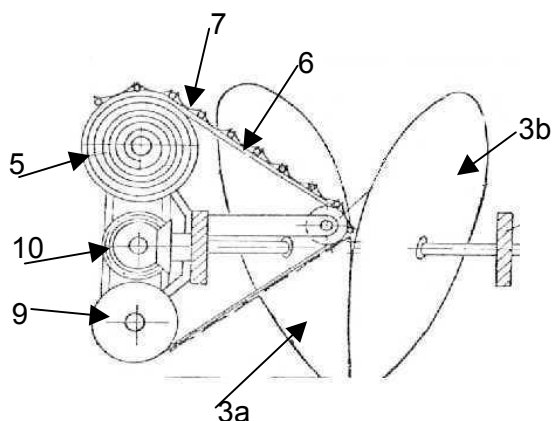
Detalhe do conjunto Transplantador (Patente 886146)
